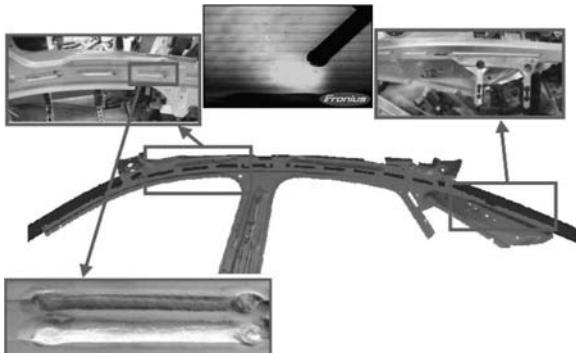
Применение гибридной лазерной МИГ сварки при изготовлении автомобилей
